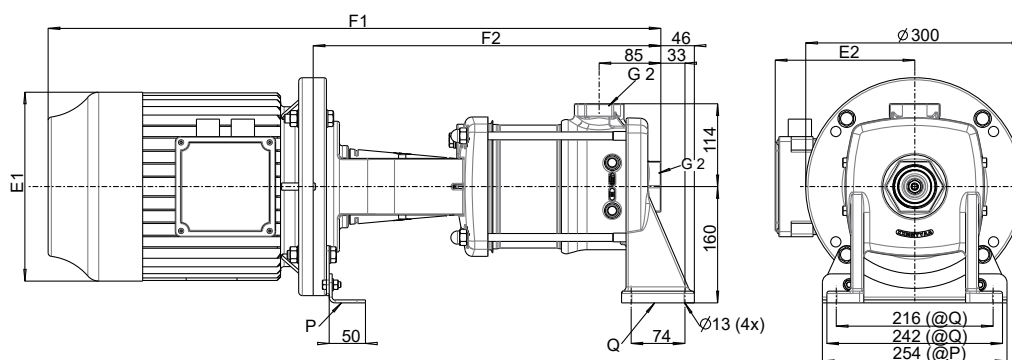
Abmessungen und Anschlüsse Movitec H(S)I 15 mit Motor V1
